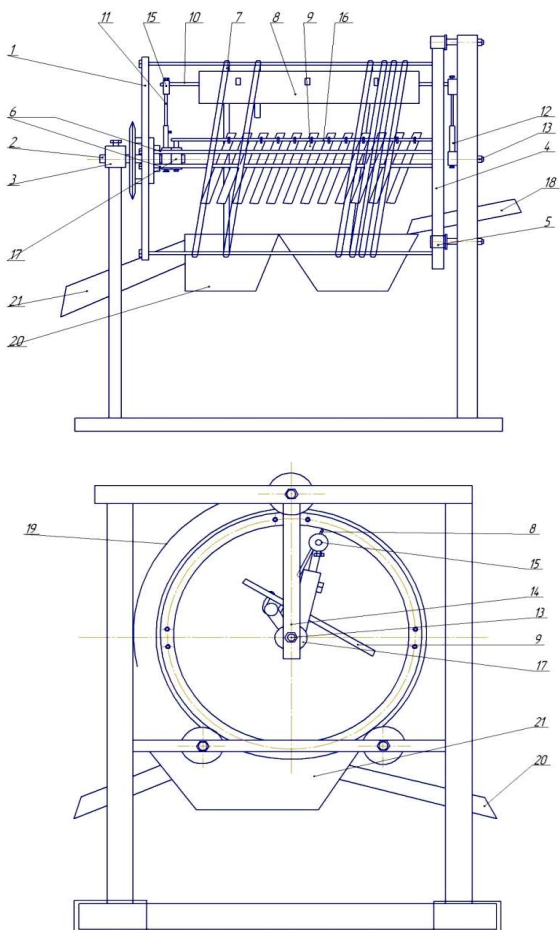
Быстроходная сортировка корнеклубнеплодов
